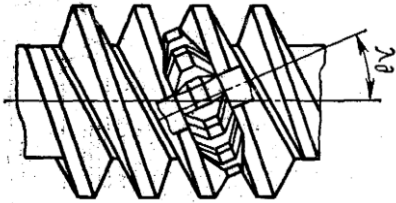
Схема нарізання циліндричного черв'яка дисковою фрезою
